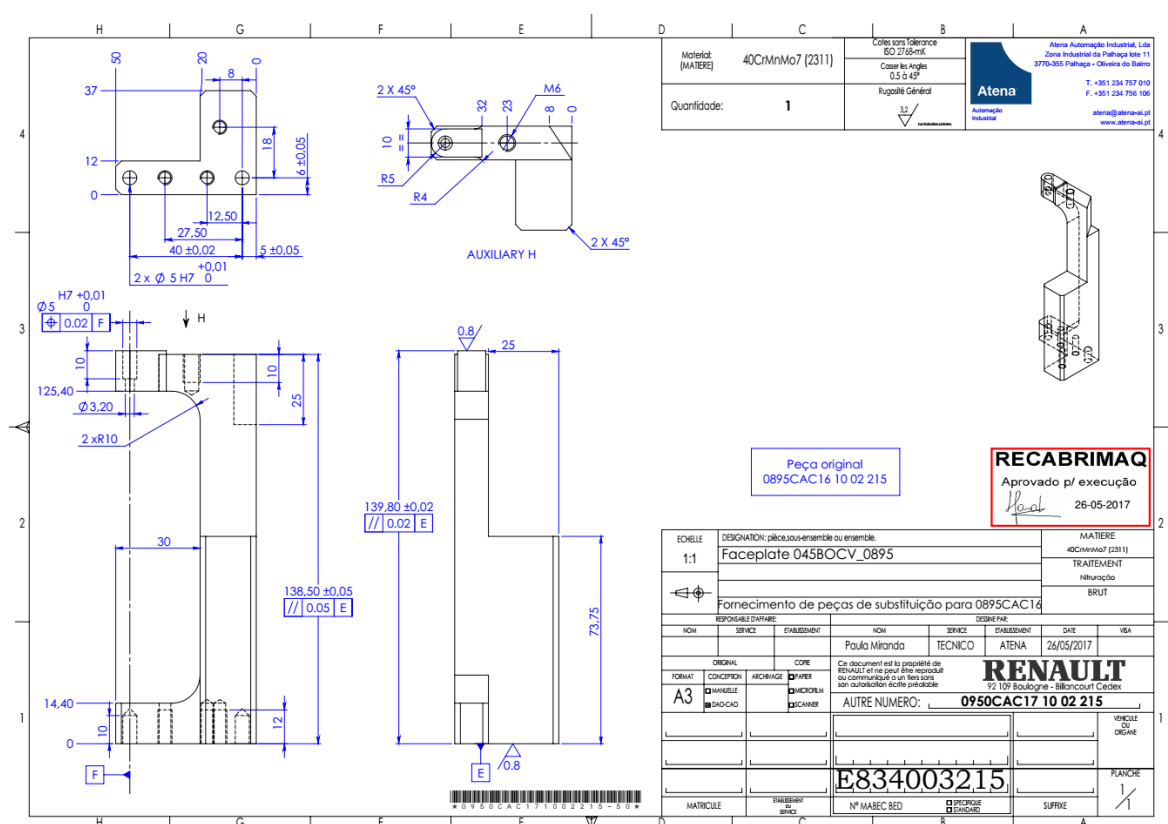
Desenho de definição da peça 0950CAC17 10 02 215
